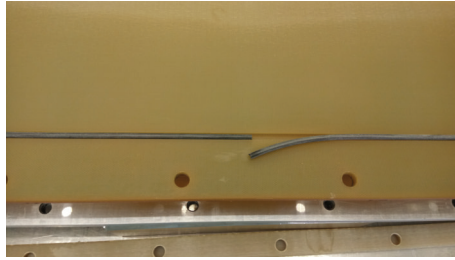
Um die Länge des Dichtringes zu bestimmen, wird der Dichtring in die Nut gelegt und so abgeschnitten, dass er wenige Millimeter zu lang ist.
